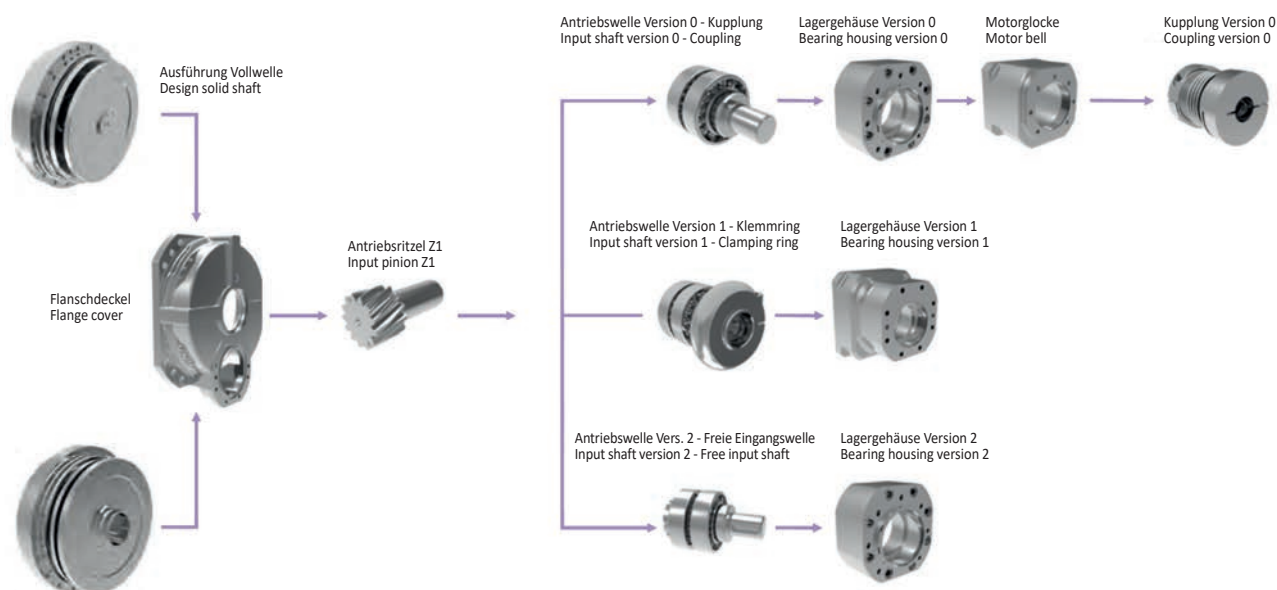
Versionen für Motoranbau | Fig.1: Versions for motor mounting
